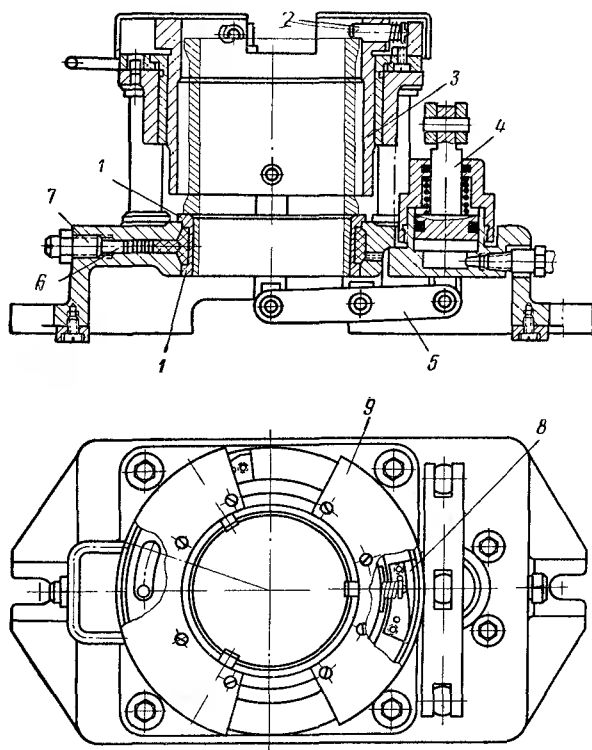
Приспособление для установки гильзы цилиндров при растачивании и хонинговании
